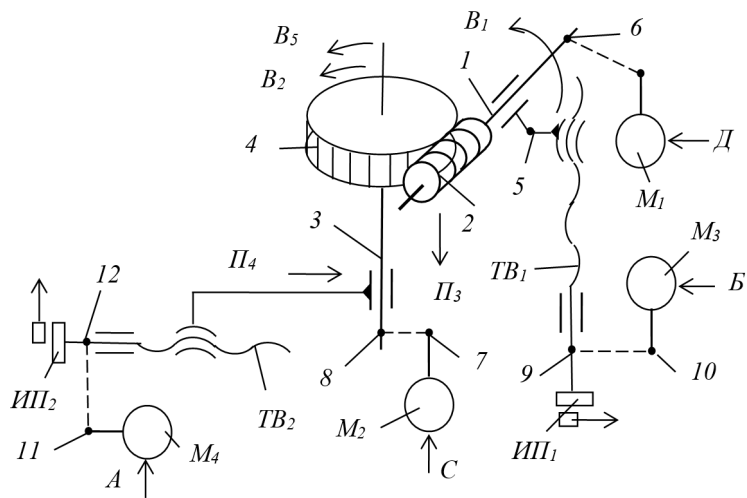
Схема приводов зубофрезерного станка для обработки колес с наклонными зубьями
